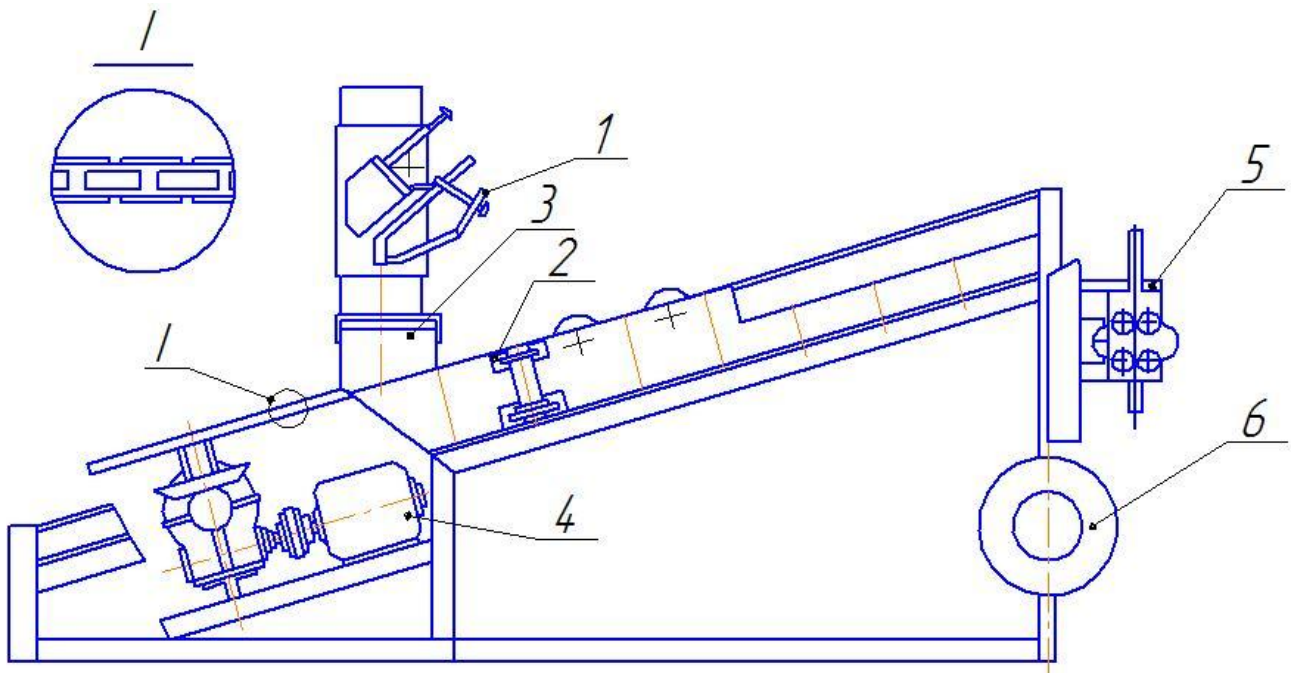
Общий вид установки для электрошлаковой наплавки: 1 – аппарат А-820 К; 2 – конвейерная часть; 3 - кристаллизатор; 4 – привод; 5 – подающий механизм; 6 – бухта с проволокой
